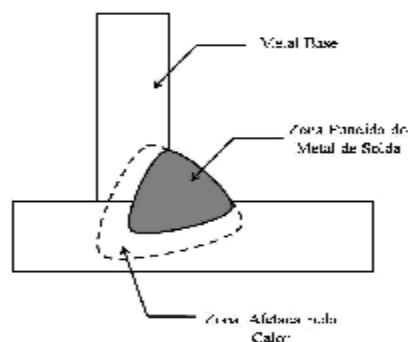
Seção transversal de uma junta soldada.
